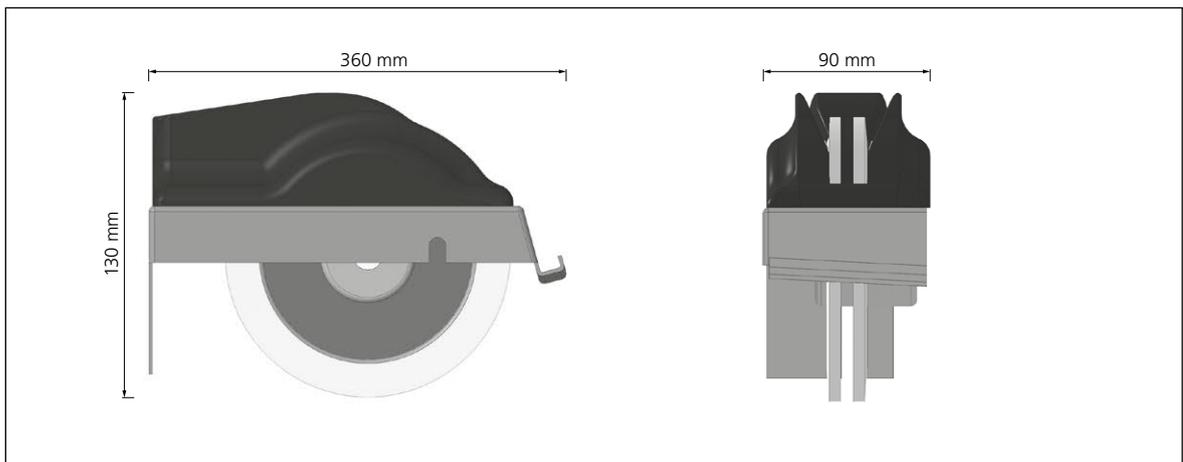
HV 150 Seitenansicht und Vorderansicht (Abmessungen in mm)
